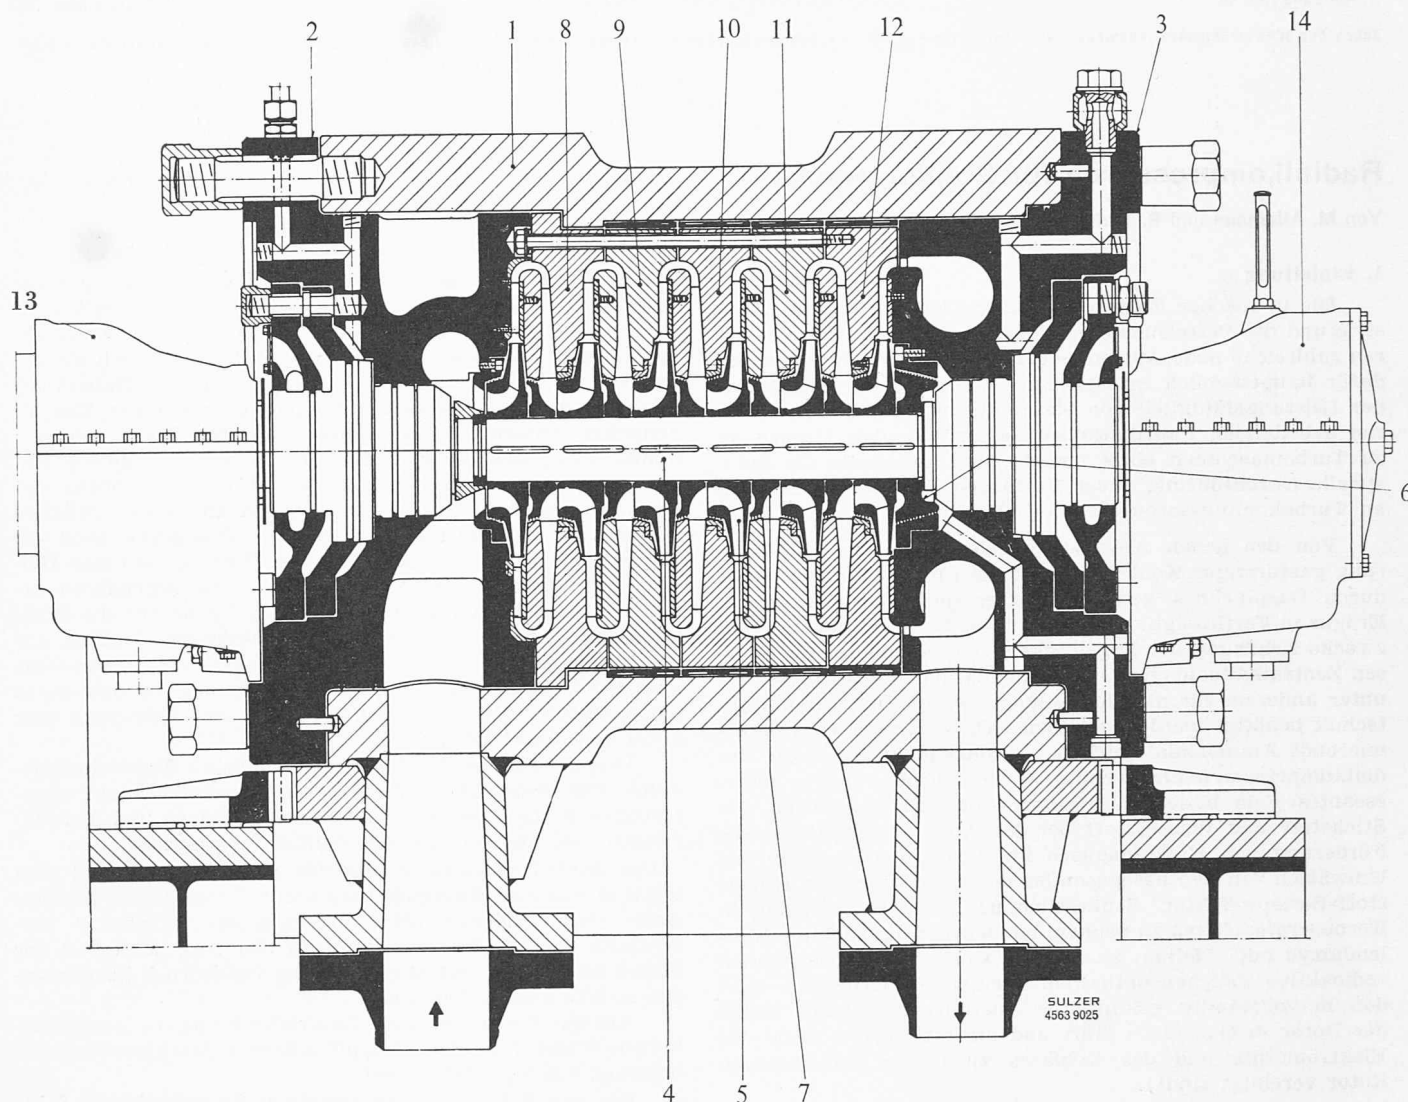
Längsschnitt durch einen Sulzer-Radial-Kompressor, Typ RCX -6N-28, für hohe Drücke, mit senkrecht zur Maschinenachse verlaufender Trennung
